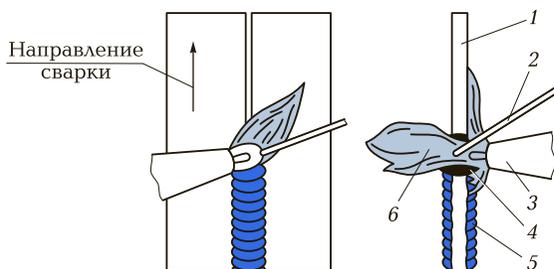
Схема сварки сквозным валиком:
